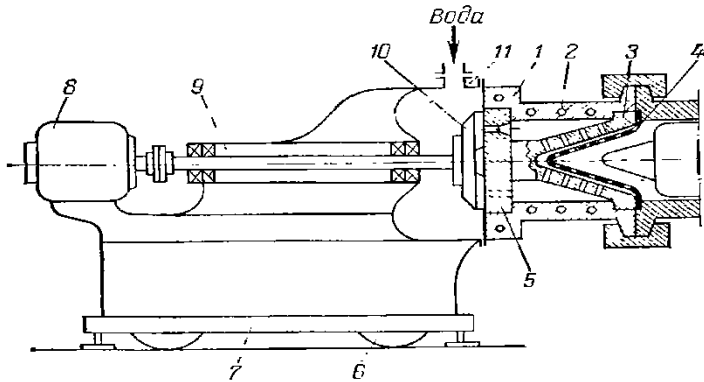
Гранулятор із різкою на решітці у водяному середовищі: 1 – корпус; 2 – канали для обігріву; 3 – конічні ґрати; 4 – фільтрувальні сітки; 5 – гранульована фільера; 6 – колеса станини; 7 – станина; 8 – привід; 9 – вал; 10 – ножова головка; 11 – камера
